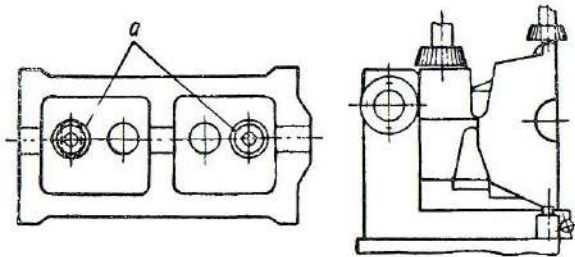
Базування блока невеликих розмірів під час обробки допоміжних баз
